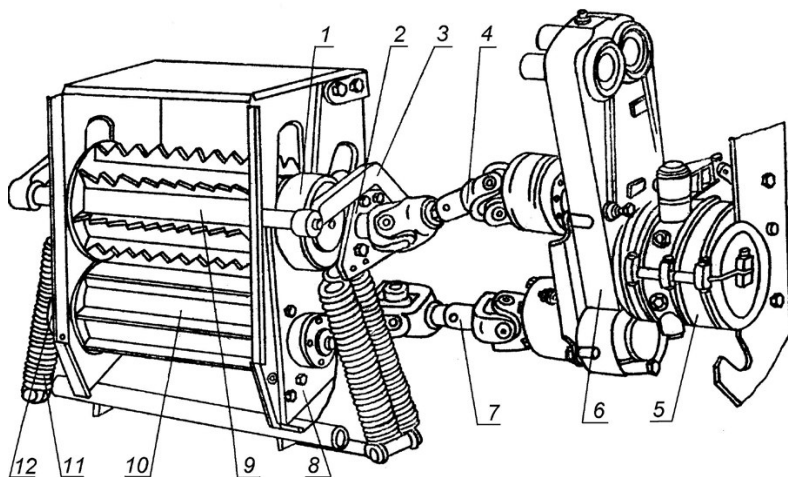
Питающий аппарат: 1 – редуктор верхних валцов; 2 – навеска; 3 – рычаг; 4, 7 – карданные валы; 5 – коробка передач; 6 – редуктор; 8 – корпус; 9 – верхний валец; 10 – нижний валец; 11 – пружина; 12 – редуктор нижних валцов
